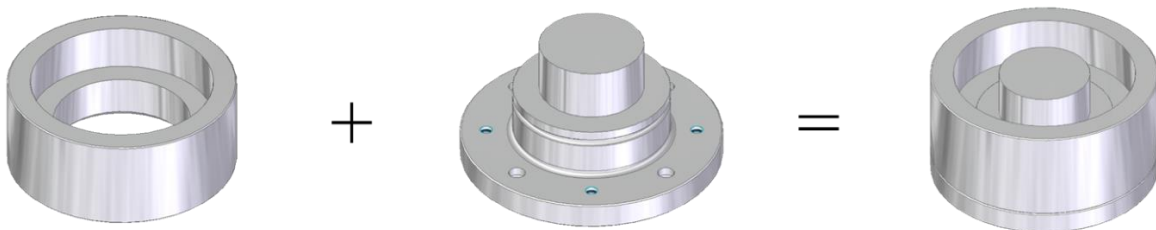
Diseño del molde de aluminio para fabricación de las probetas.
